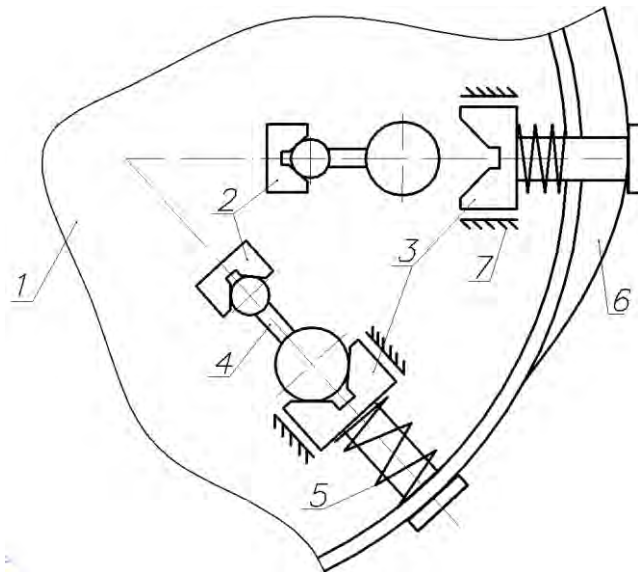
Схема приспособления для крепления заготовок на вращающемся столе 1 карусельно-фрезерного станка с автоматизированным зажимом.
